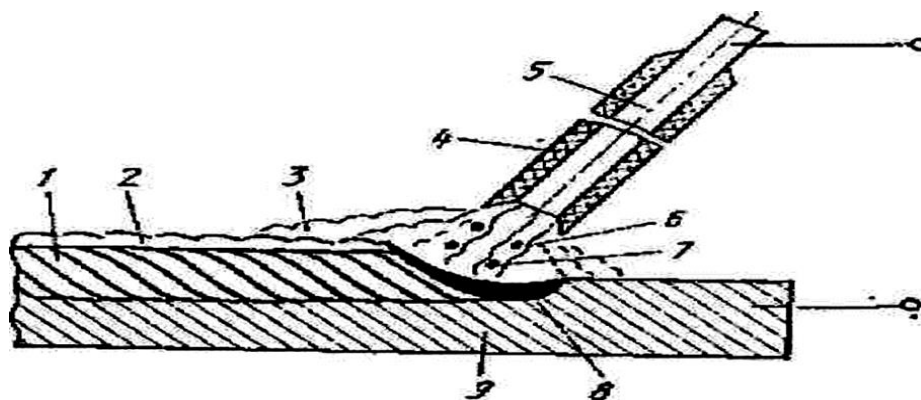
Схема процесса ручной дуговой сварки покрытым электродом: 1 - сварной шов; 2 - шлаковая корка; 3 - защитная газовая атмосфера; 4 - электродное покрытие; 5 -электродный стержень; 6 - электрическая дуга; 7 - капли электродного металла; 8 - сварочная ванна; 9 - заготовка;
